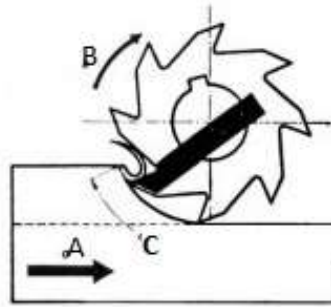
Operações de fresagem: a) movimento de avanço; b) movimento principal ou de corte; c) curso útil de uma navalha [44].
